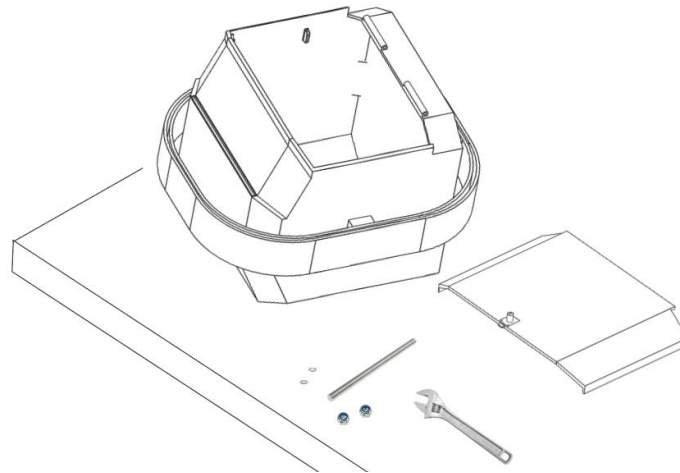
Secuencia 4. Ensamblaje subconjunto 1.1
